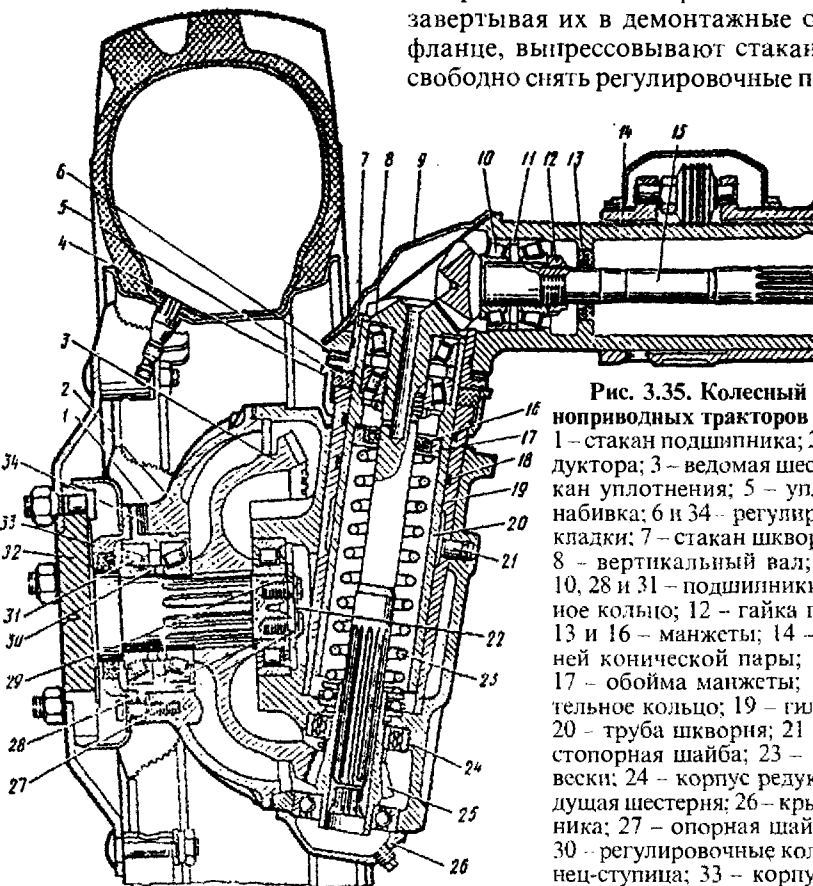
Колесный редуктор полноприводных тракторов МТЗ и ЮМЗ: 1 – стакан подшипника; 2 – крышка редуктора; 3 – ведомая шестерня; 4 – стакан уплотнения; 5 – уплотнительная набивка; 6 и 34 – регулировочные прокладки; 7 – стакан шкворневой трубы; 8 – вертикальный вал; 9 – крышка; 10, 28 и 31 – подшипники; 11 – распорное кольцо; 12 – гайка подшипников; 13 и 16 – манжеты; 14 – корпус верхней конической пары; 15 – полуось; 17 – обойма манжеты; 18 – уплотнительное кольцо; 19 – гильза шкворня; 20 – труба шкворня; 21 – штифт; 22 – стопорная шайба; 23 – пружина подвески; 24 – корпус редуктора; 25 – ведущая шестерня; 26 – крышка подшипника; 27 – опорная шайба; 29 – болт; 30 – регулировочные кольца; 32 – фланец-ступица; 33 – корпус манжеты
